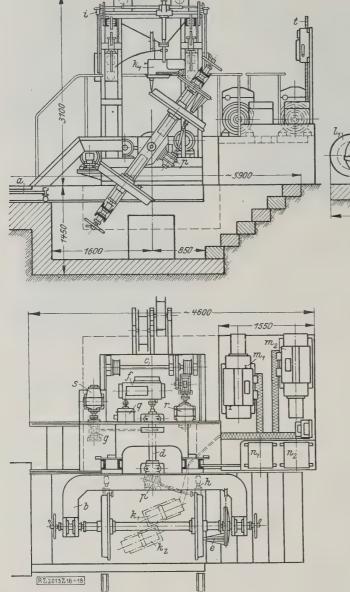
Selbsttätige Spurkranz-Schweißmaschine der Siemens-Schuckertwerke.
